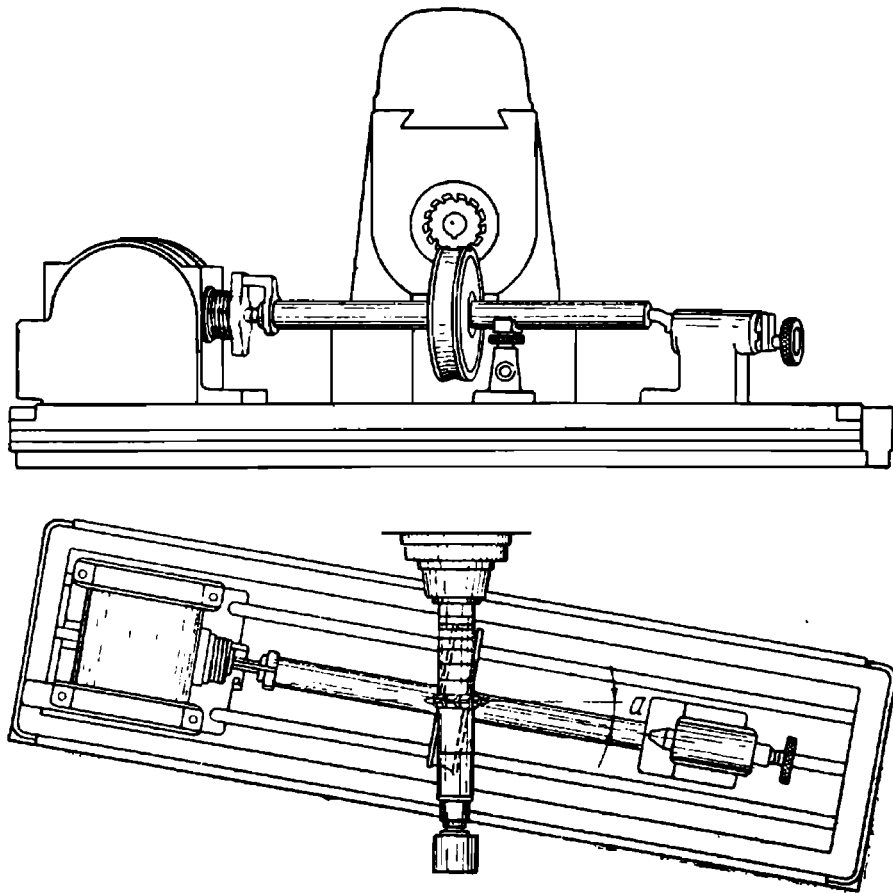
Установка стола станка при предварительном нарезании червячного колеса
